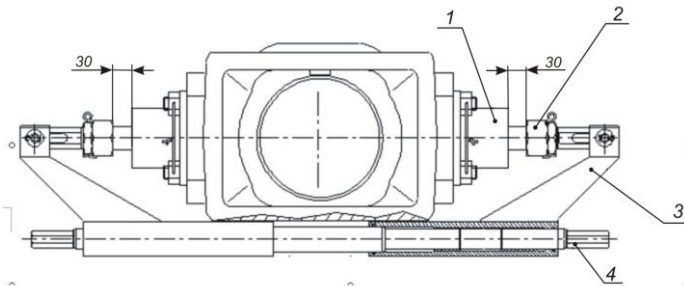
Положение сцепки БСУ-4 в режиме готовности к расцеплению: 1 – корпус автоматического замка; 2 – гайка упорная (гайка штока стопора); 3 – кронштейн механизма расцепления; 4 – хвостовик винта
